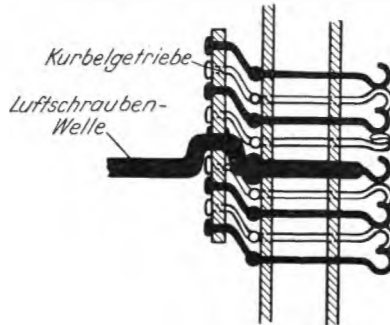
Aufgeteilter Gummimotor mit Kurbelgetriebe.
